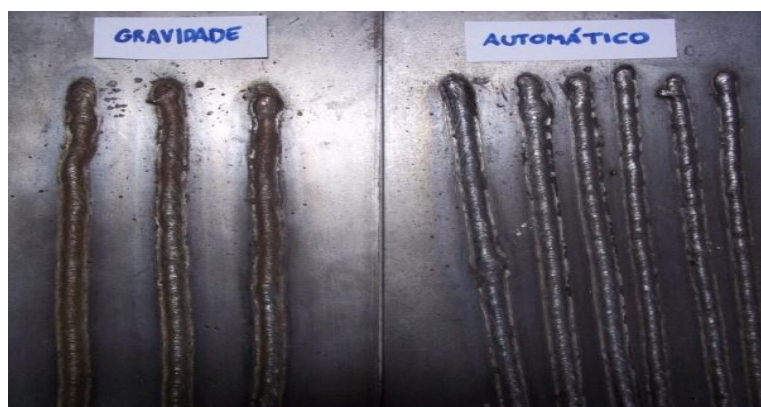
Cordões de solda realizados com eletrodos E7018
